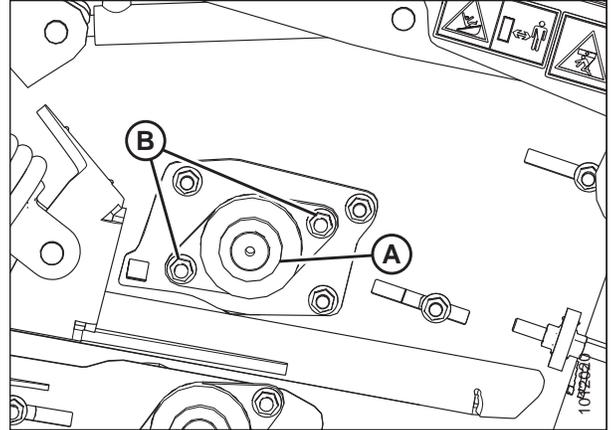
Rodillo de mando de la cama frontal del lado derecho
